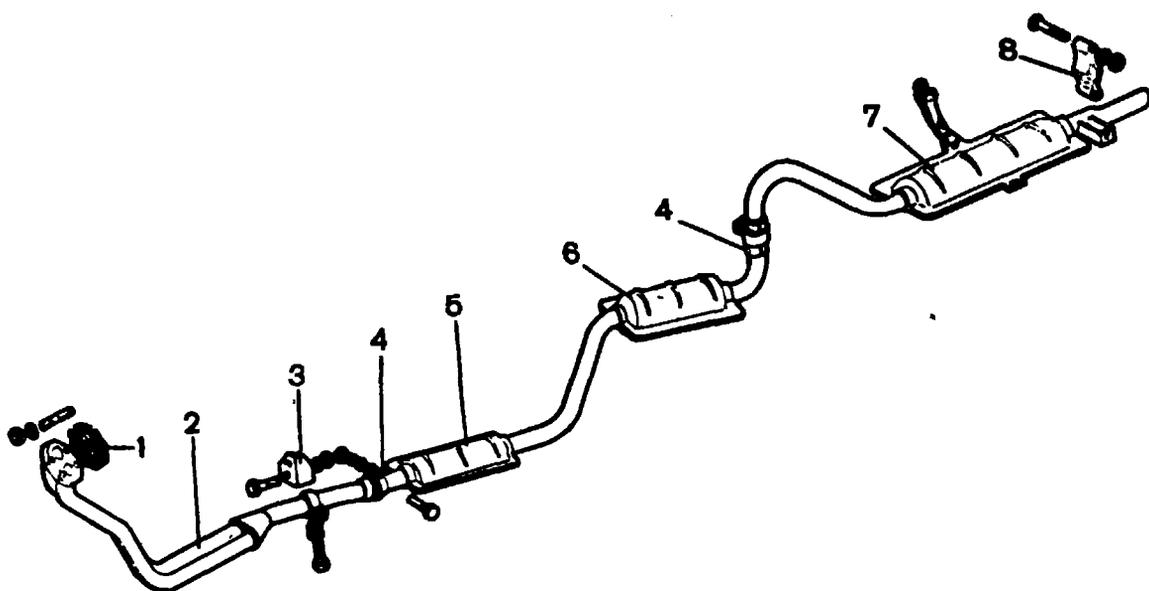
Выпуск отработавших газов: 1 - прокладка; 2 - приемная труба глушителей; 3 - кронштейн крепления приемной трубы к коробке передач; 4 - хомут для соединения труб глушителей; 5 - передний дополнительный глушитель; 6 - задний дополнительный глушитель; 7 - основной глушитель; 8 - подушка крепления выпускной трубы основного глушителя
